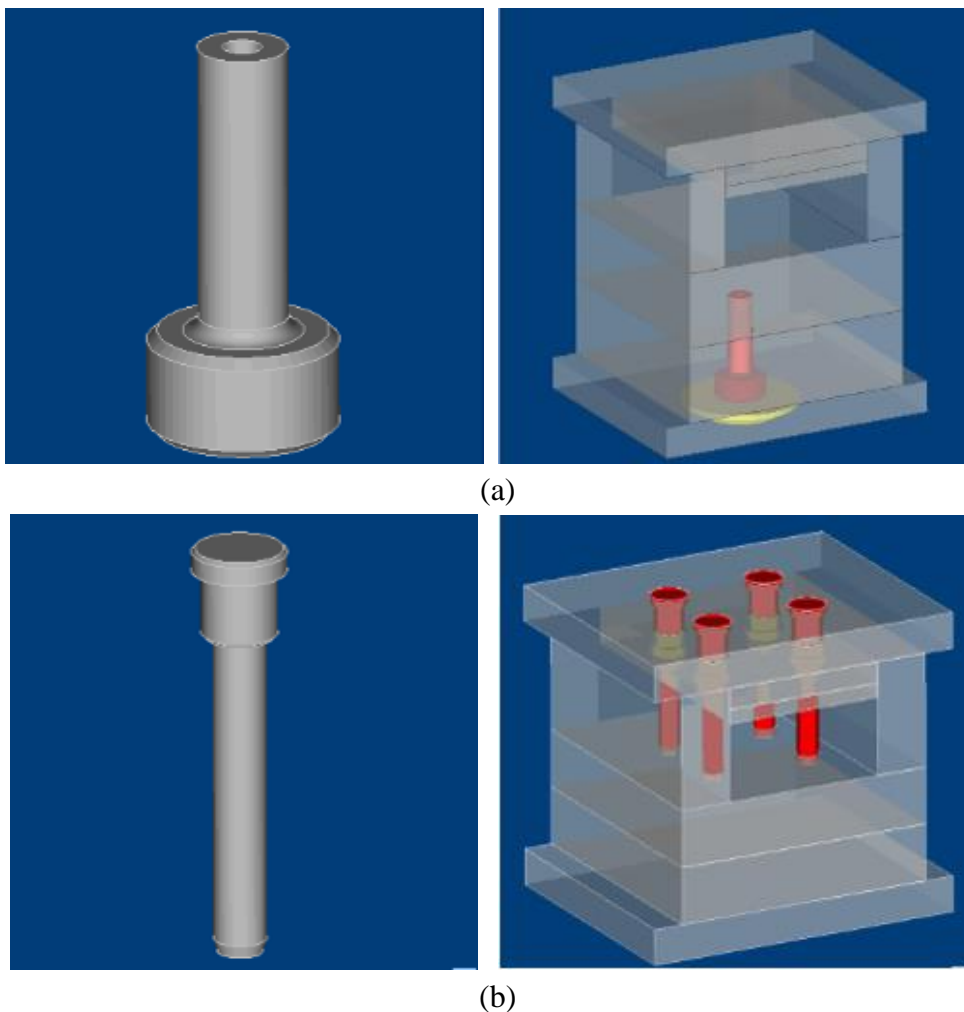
Acessórios de injeção e extração: Injetor principal (a) e guias das chapas de extração (b) (Moldes, 2019).
